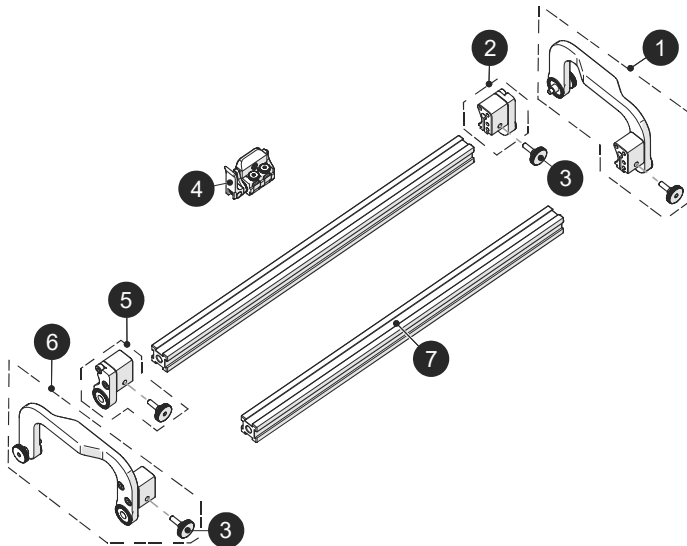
Schweißprüfkopf-Halterrahmen
